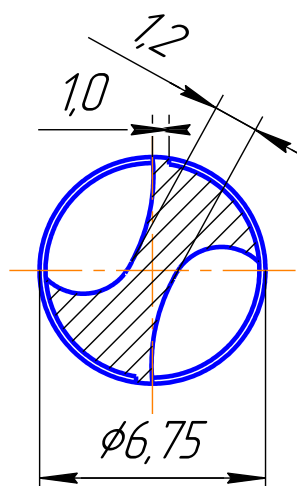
Эскиз зуба и стружечной канавки
